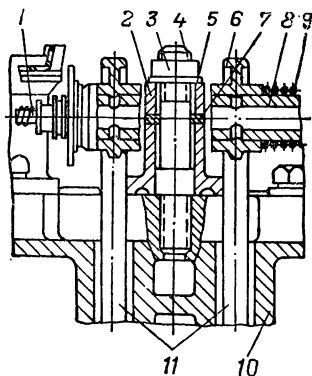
Крепление стойки оси коромысел клапанов к головке блока цилиндров: 1 — маслопровод; 2 — стойка оси коромысел; 3 — гайка; 4 — шпилька; 5 — шайба; 6 — коромысло; 7 — чека; 8 — ось; 9 — большая пружина; 10 — головка блока цилиндров; 11 — толкающая штанга
